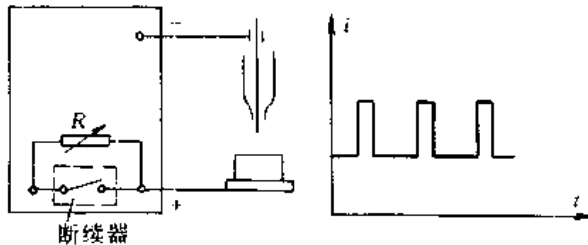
单电源供电 TIG 焊原理示意图
